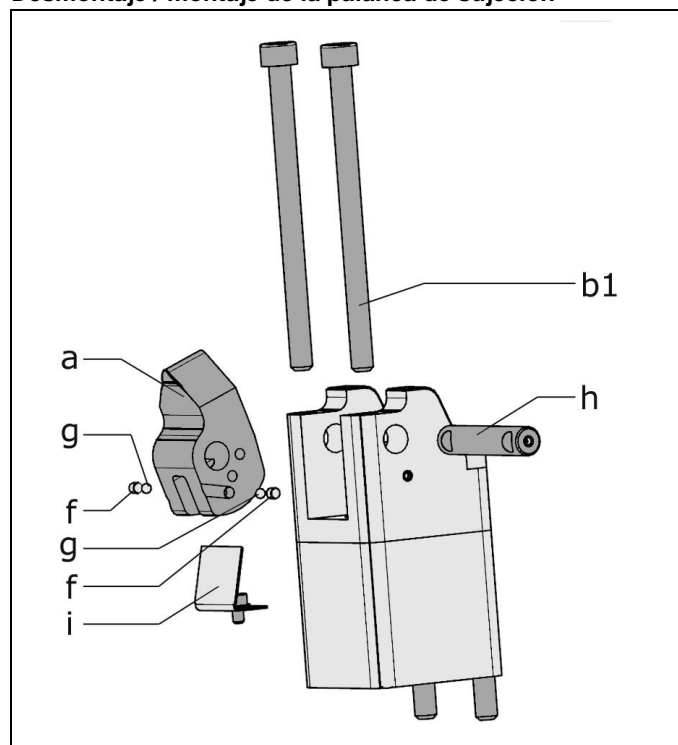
Desmontaje / montaje de la palanca de sujeción
